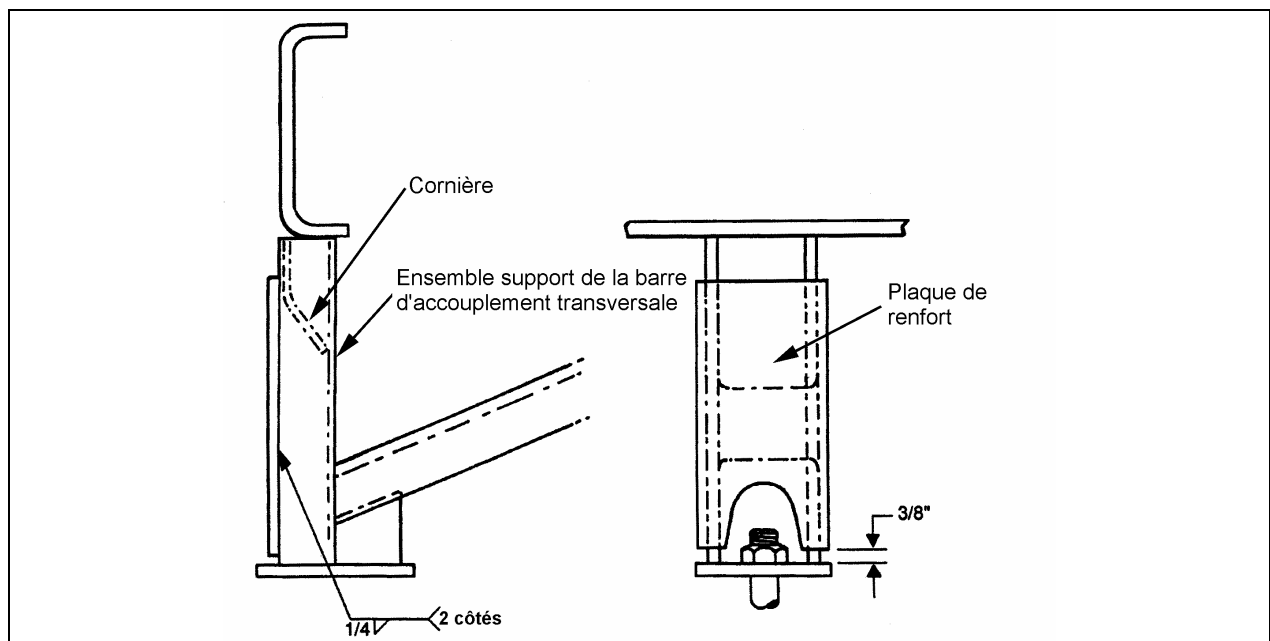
INSTALLATION DE LA CORNIÈRE ET DE LA PLAQUE DE RENFORT
